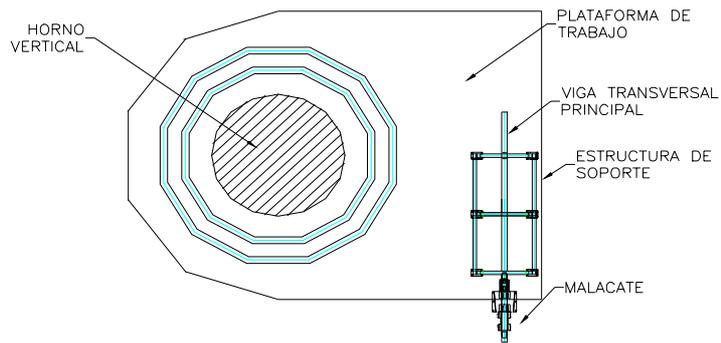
VISTA DE PLANTA DE GRÚA CORREDIZA.
